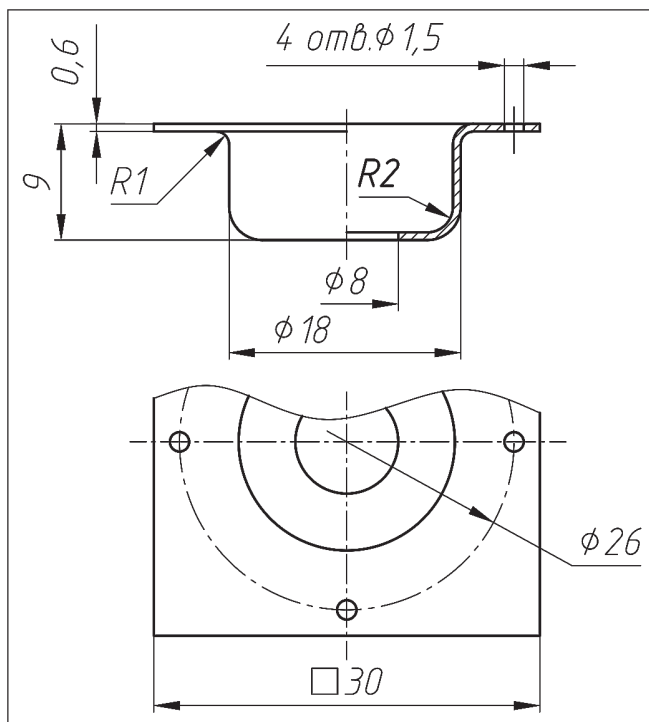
Эскиз детали «Колпачок» с натурального образца
